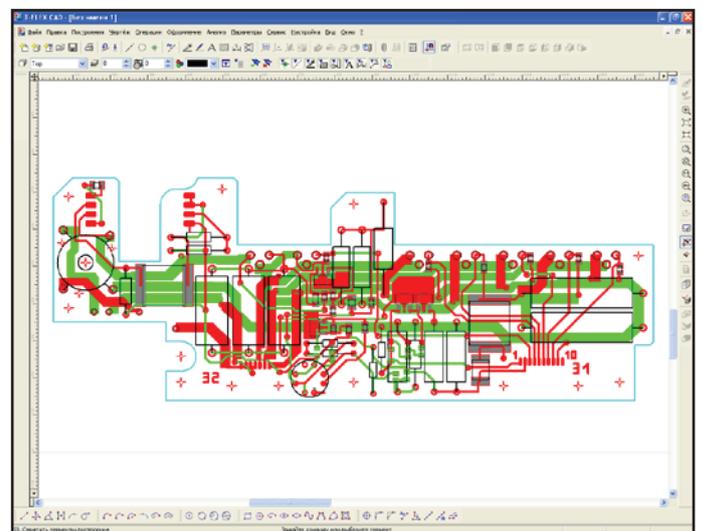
Файл топологии ПП, импортированный в T-Flex CAD из P-CAD
